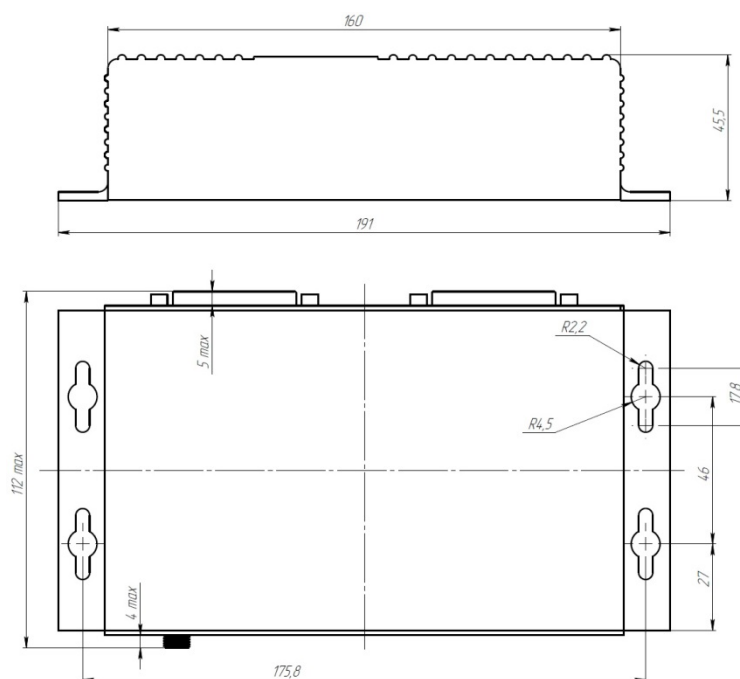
Габаритный чертеж МСКЮ.468351.003-02
